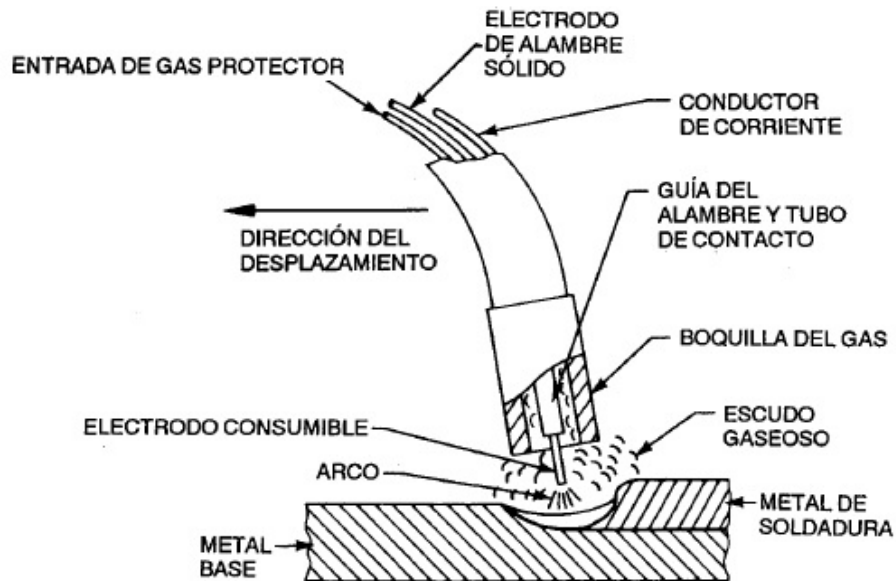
Proceso de soldadura por arco metálico y gas [43].
